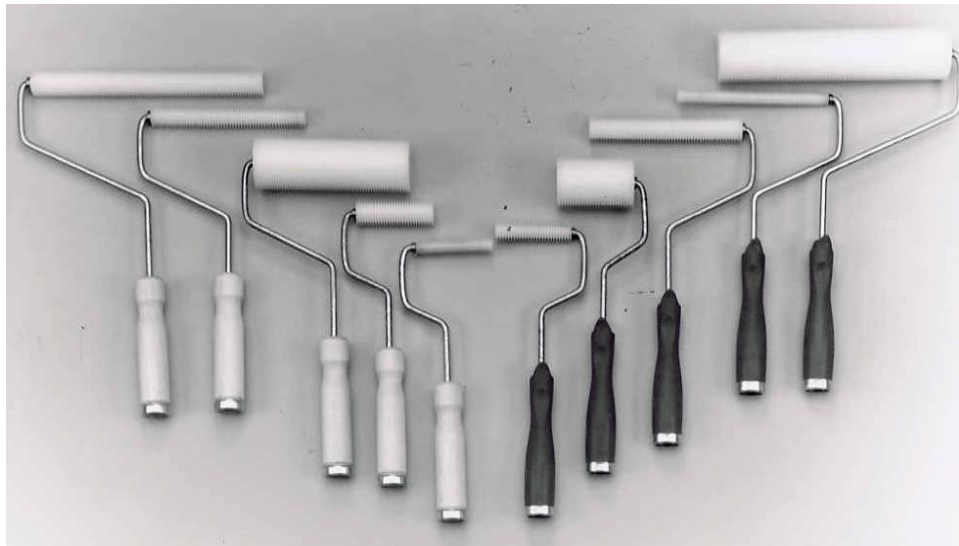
Deluxe & Quick Release Aluminum Paddle Rollers
